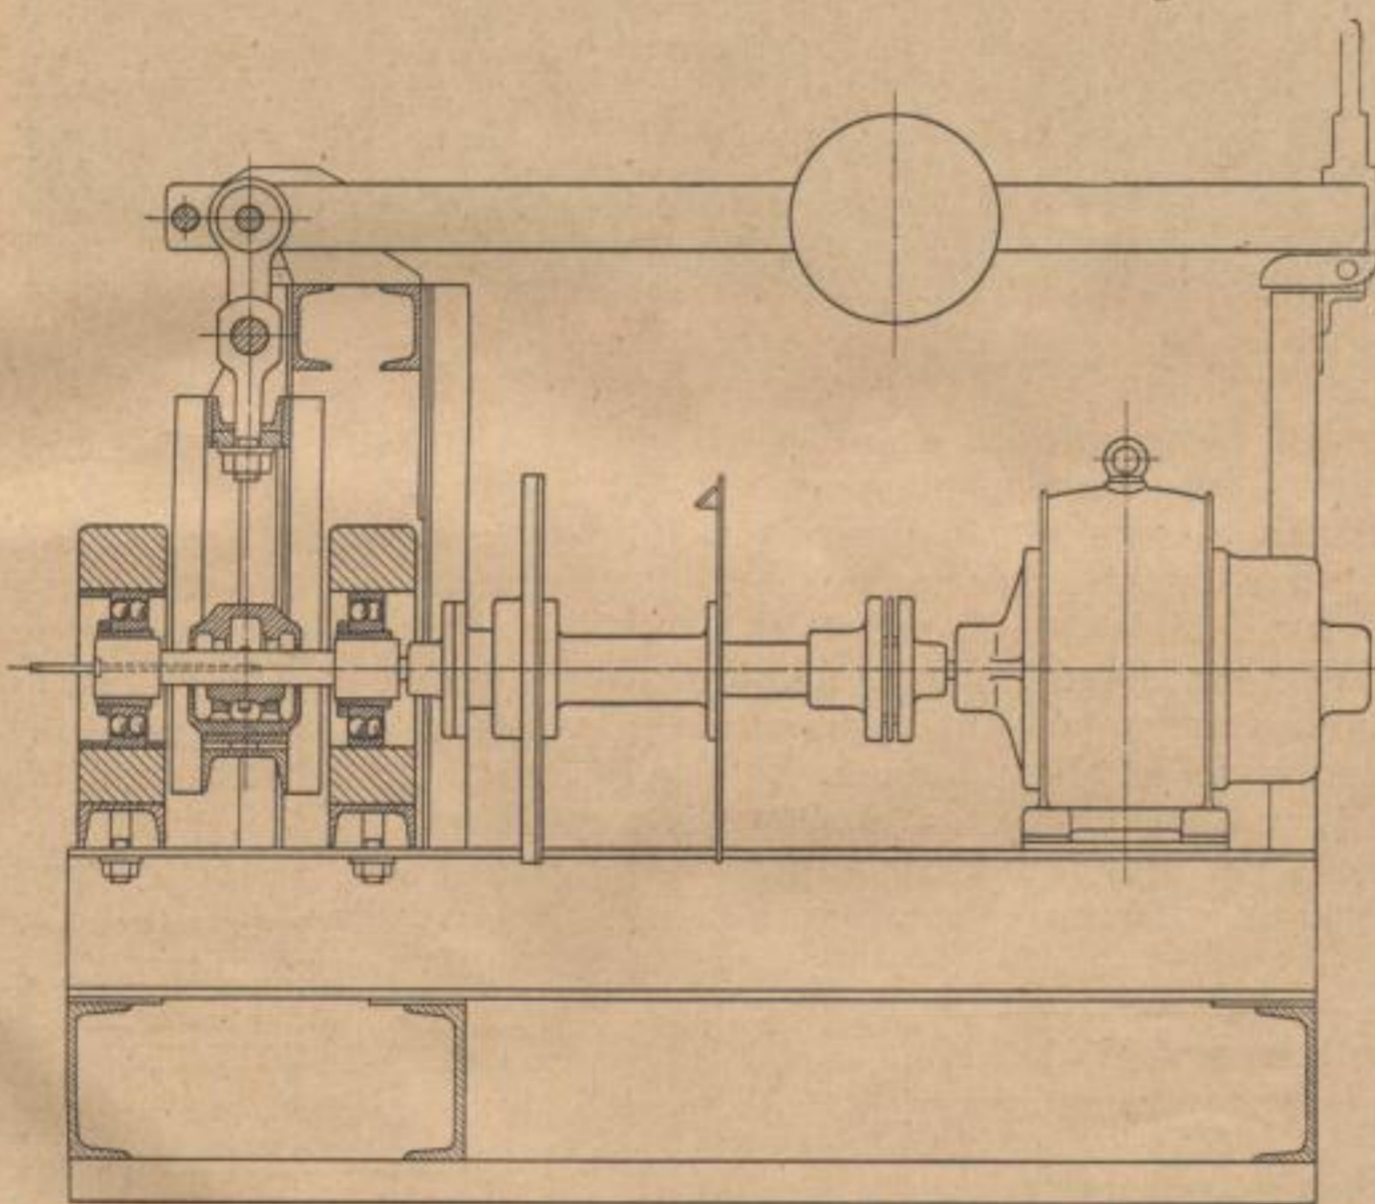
Lagerprüfstand des Versuchsfeldes für Maschinen-Elemente an der T. H. Berlin. Baurat Kammerer und Welter.
